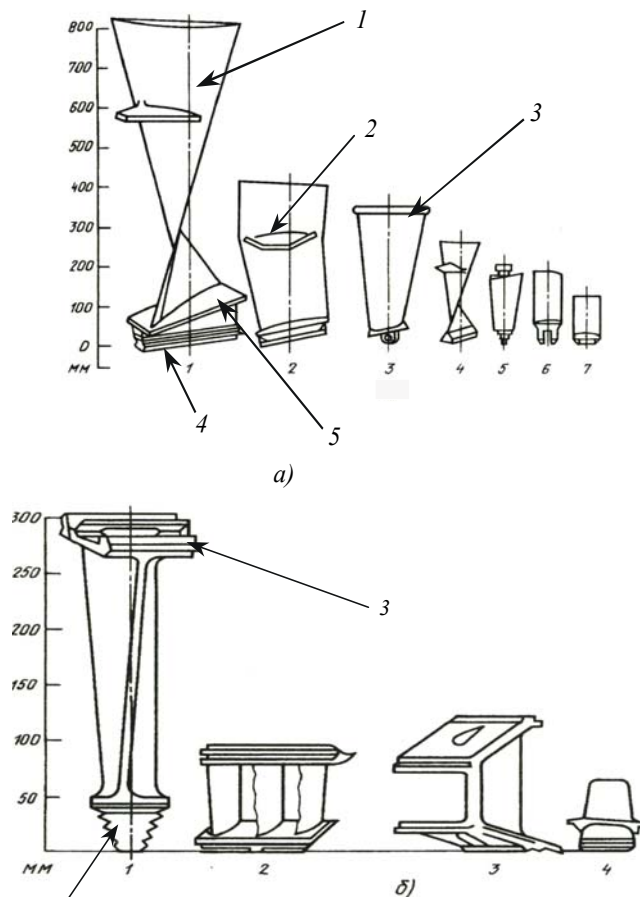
Внешний вид лопаток [1]: а - компрессора двигателя; б - турбины двигателя:
